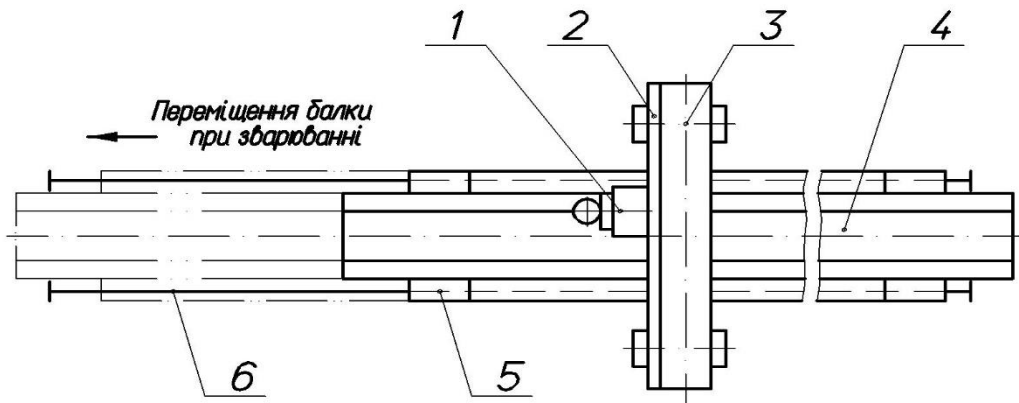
Схема зварювання балки при переміщенні її кантувачем зі швидкістю зварювання:
